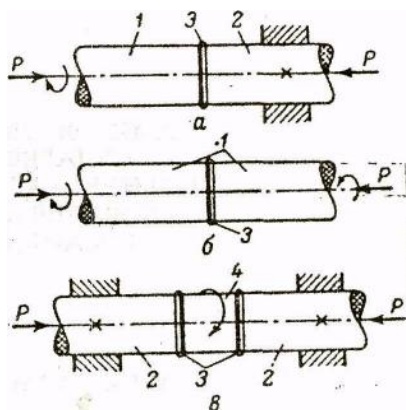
Схема сварки трением с использованием вращения
